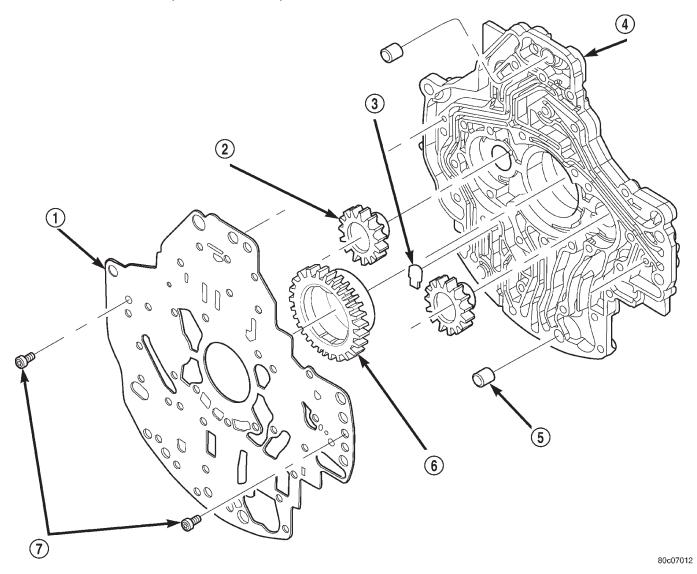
Cuerpo y engranajes de la bomba de aceite
